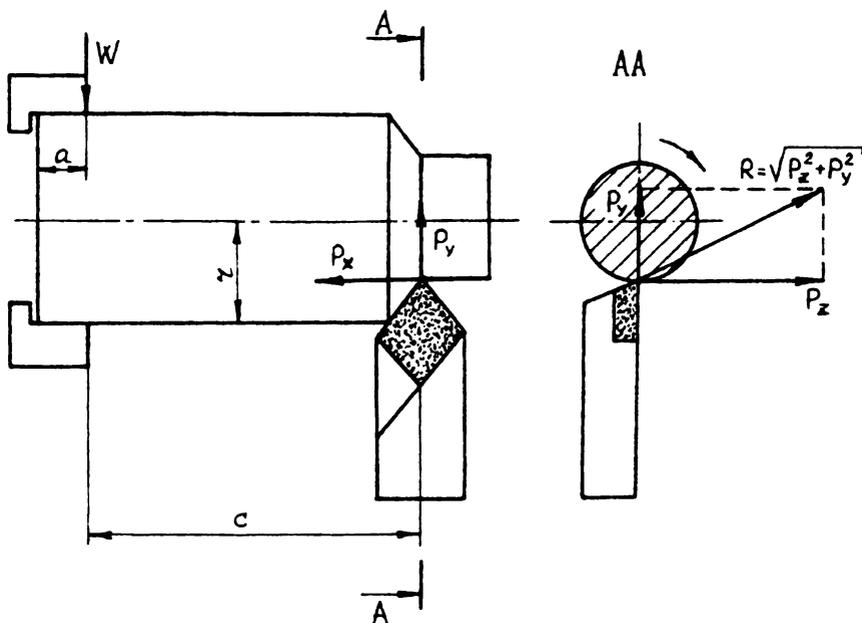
Схема для расчета необходимой силы закрепления заготовки при токарной обработке
